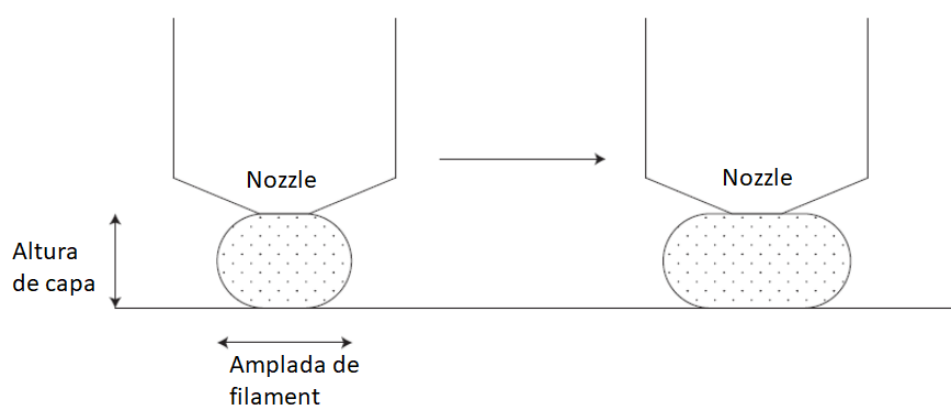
Diferència entre una impressió amb sobre-extrusió (esquerra) i sense (dreta) [20]
